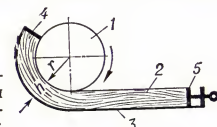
Принципиальная схема гнутья древесины: 1 — шаблон; 2 — заготовка; 3 — шина; 4 — неподвижный торцевой упор; 5 — подвижный торцевой упор.
